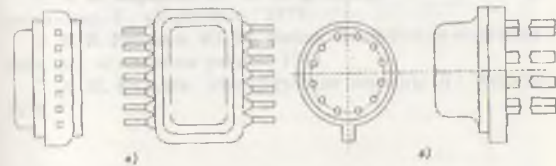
Корпуса ИМС: а) четырехугольной формы; б) круглой формы.
